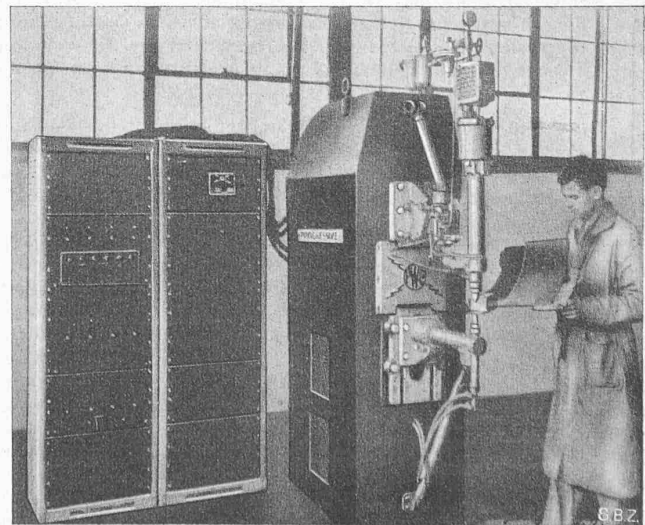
Progressive Welder-Punktschweissmaschine für Leichtmetalle
